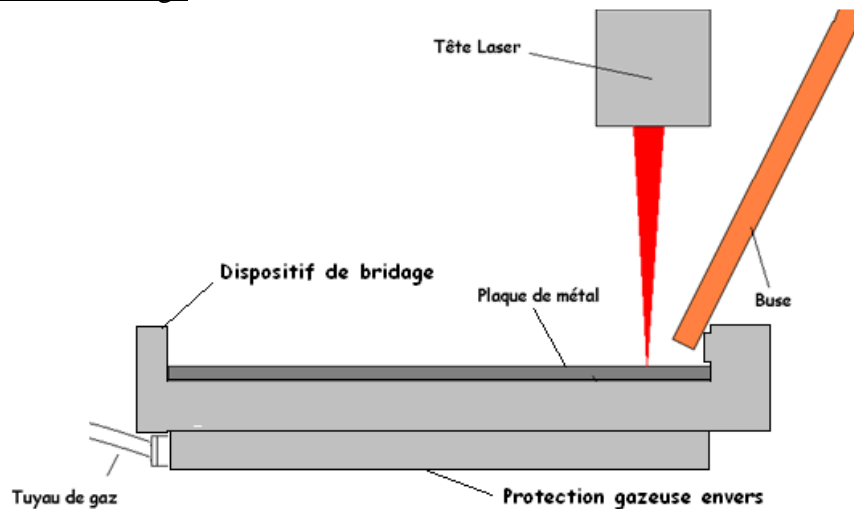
La configuration de soudage pour l'assemblage cuivre-inox par laser.
